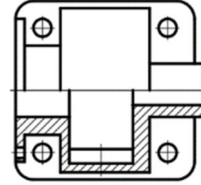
Кресленик горизонтального розрізу корпусу Б-Б
